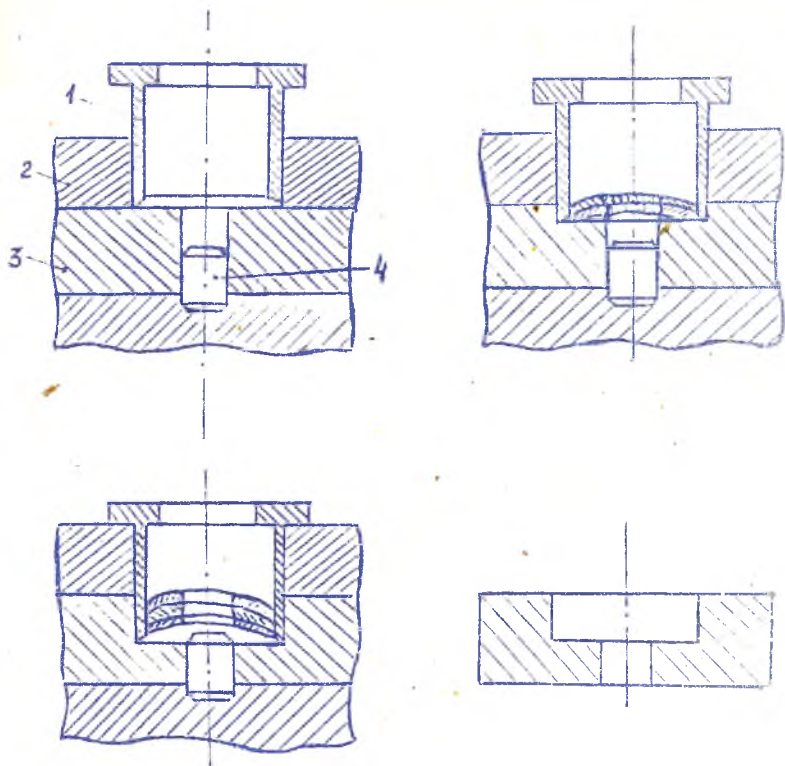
Способ получения отверстий с лунками в толстолистовых деталях из слоисто-волоконистых композиционных материалов: 1 – втулочный пуансон; 2 – направляющая плита; 3 – толстолистовая заготовка; 4 – штифт
